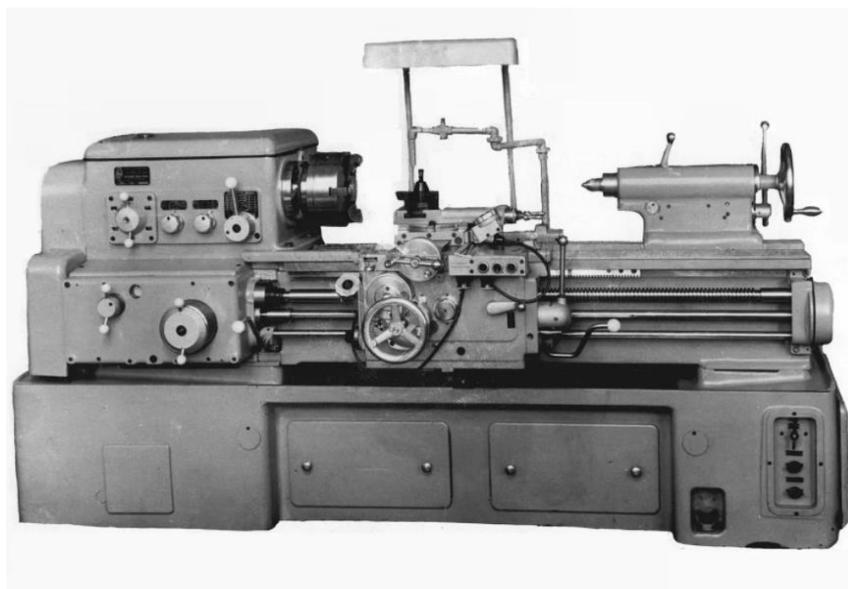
Внешний вид токарно-винторезного станка 1К62Д
